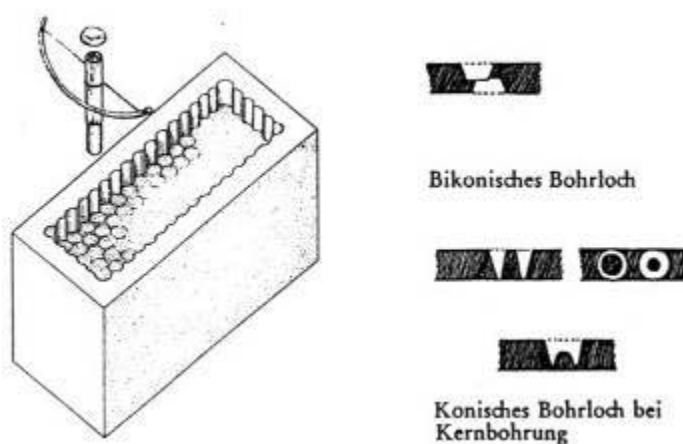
Bohrlochformen verschiedener Bohrgeräte<sup>809</sup>
